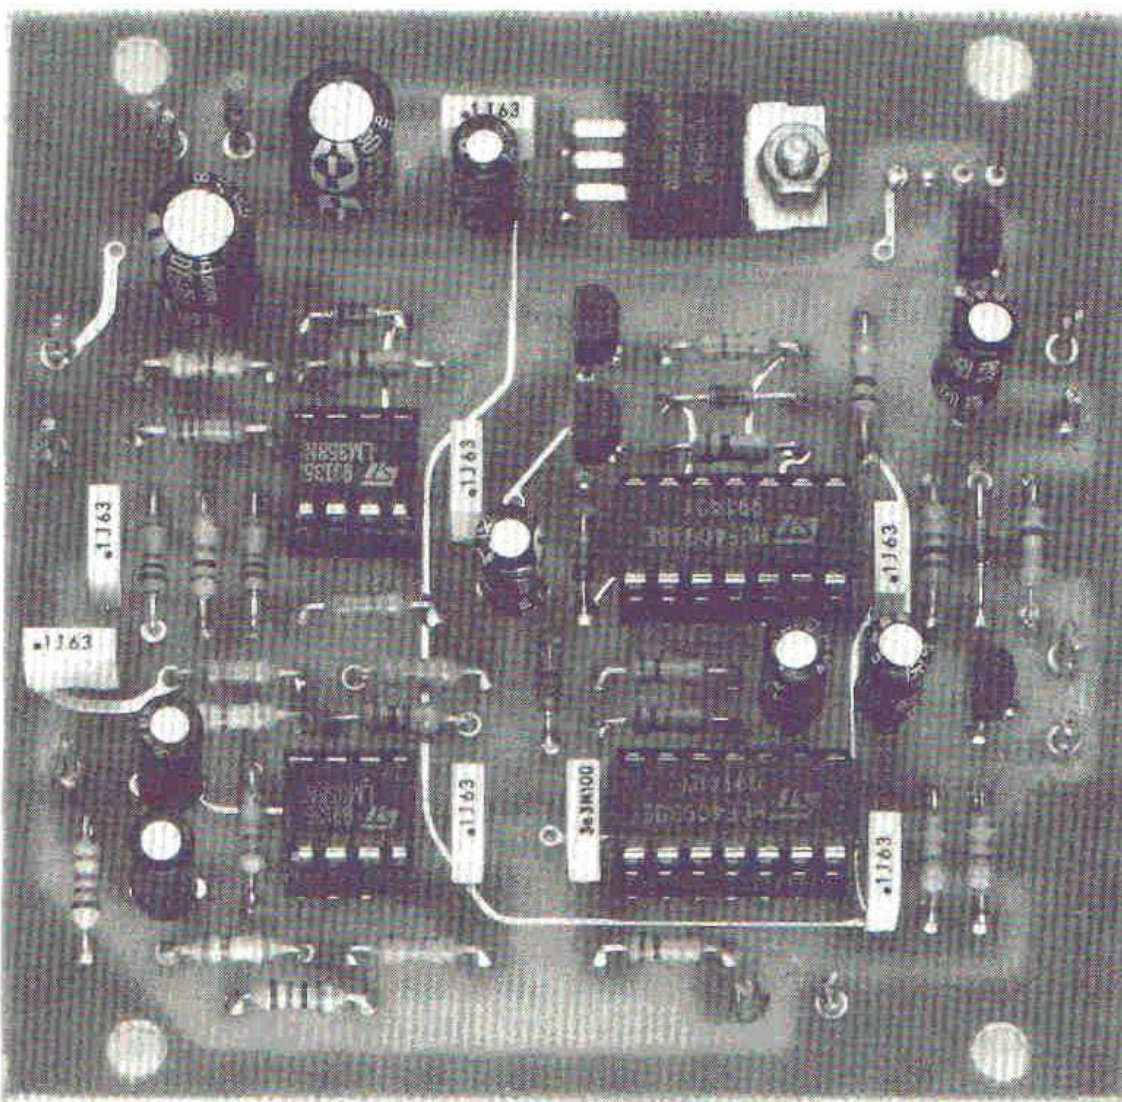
Foto notevolmente ingrandita dello stampato LX.1083, con tutti i componenti già montati. Anche se in questa foto non è visibile, lo stampato è completo di disegno serigrafico che aiuterà il lettore a trovare la giusta posizione di ogni componente.
